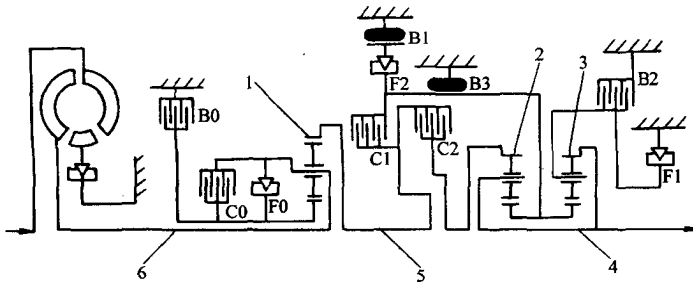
3 行星排辛普森式 4 档行星齿轮变速器的结构简图
